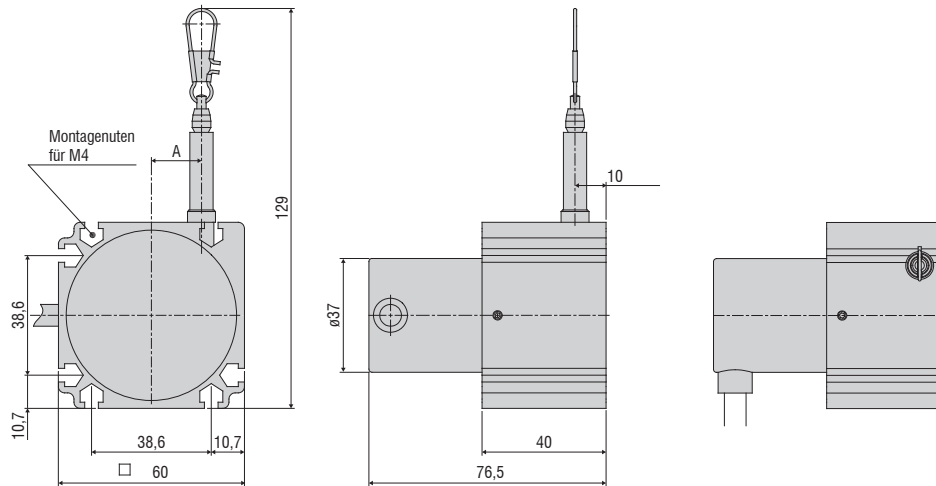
Maßzeichnung WDS- ... - P60 - CR - P, Abmessungen in mm
